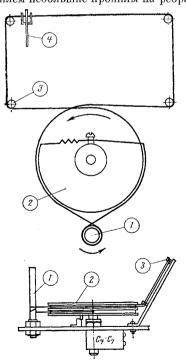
Кинематическая схема верньерного устройства: 1—ось настройки; 2—маховик; 3—направляющая шпилька; 4—указатель.
